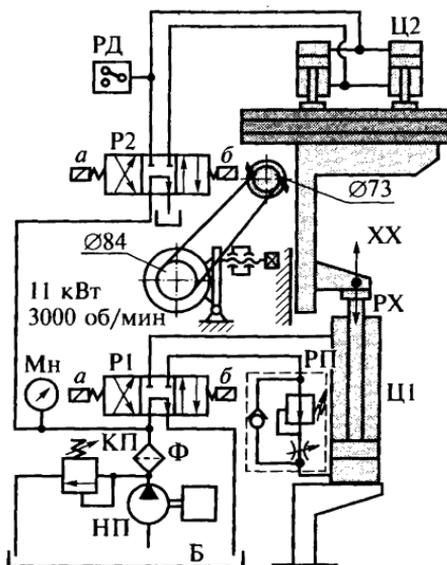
Гидрокинематическая схема шипорезного станка для выработки ящичных или клиновых шипов:
